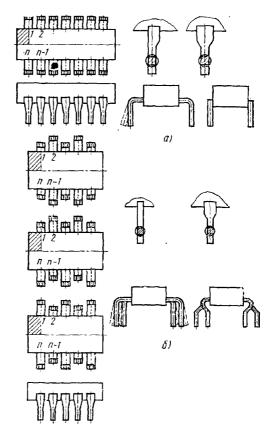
Конструкции корпусов типа 2 подтипов 21(a) и 22(б) с вариантами формовки и конструкций выводов
